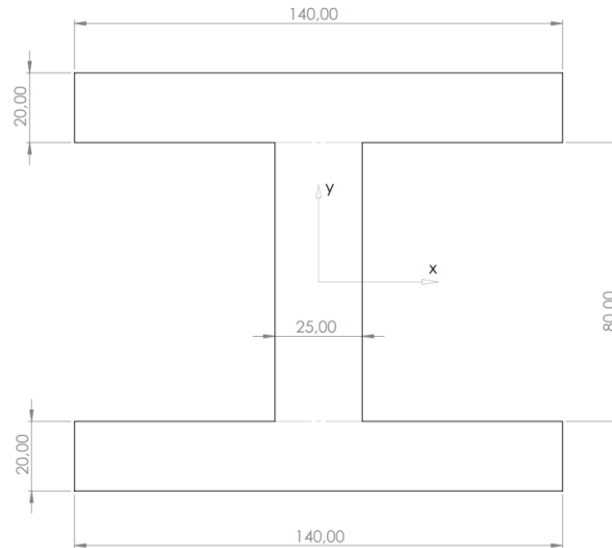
Dimensiones del nuevo diseño de la placa de presión.
